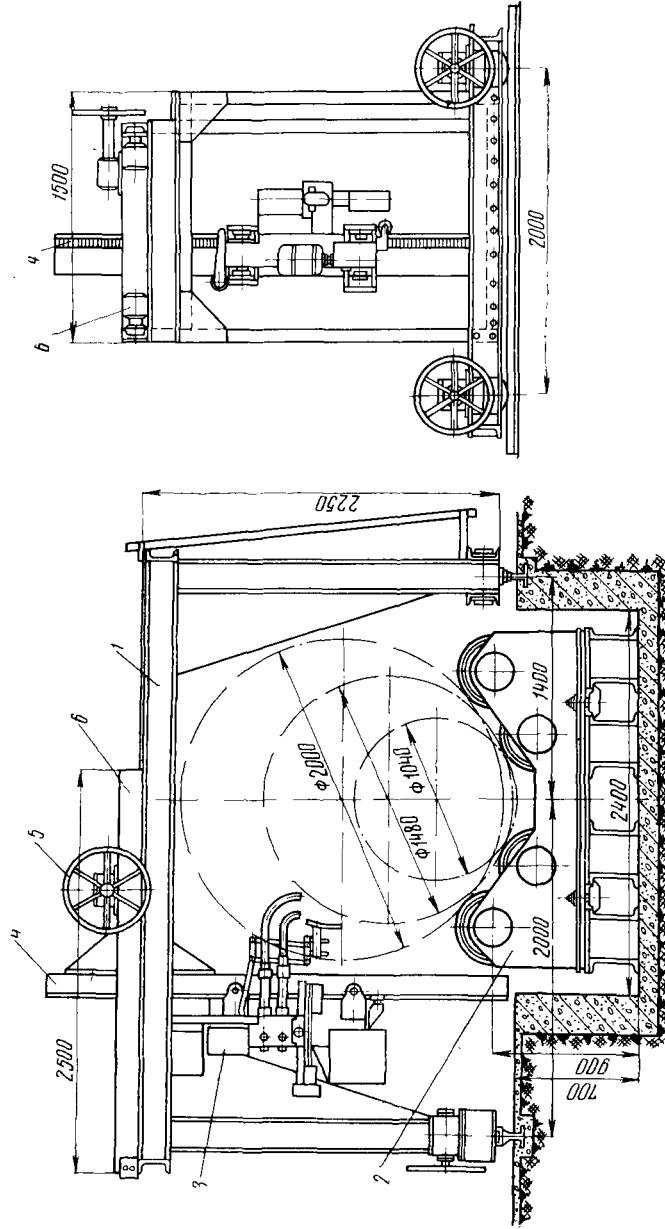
Установка для электрошлаковой сварки кольцевых швов
